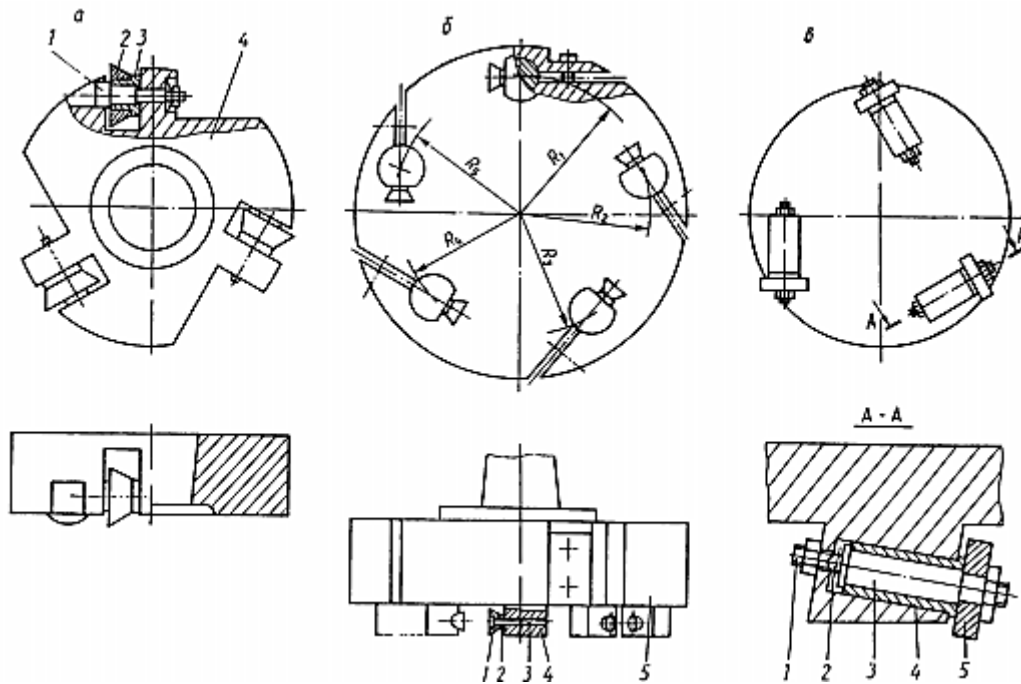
Ротаційні фрези на підшипниках ковзання[9]
